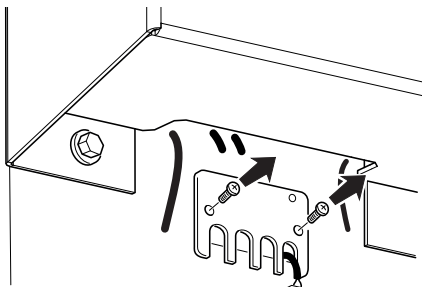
Desmontar la placa de la tarjeta de interfaz
